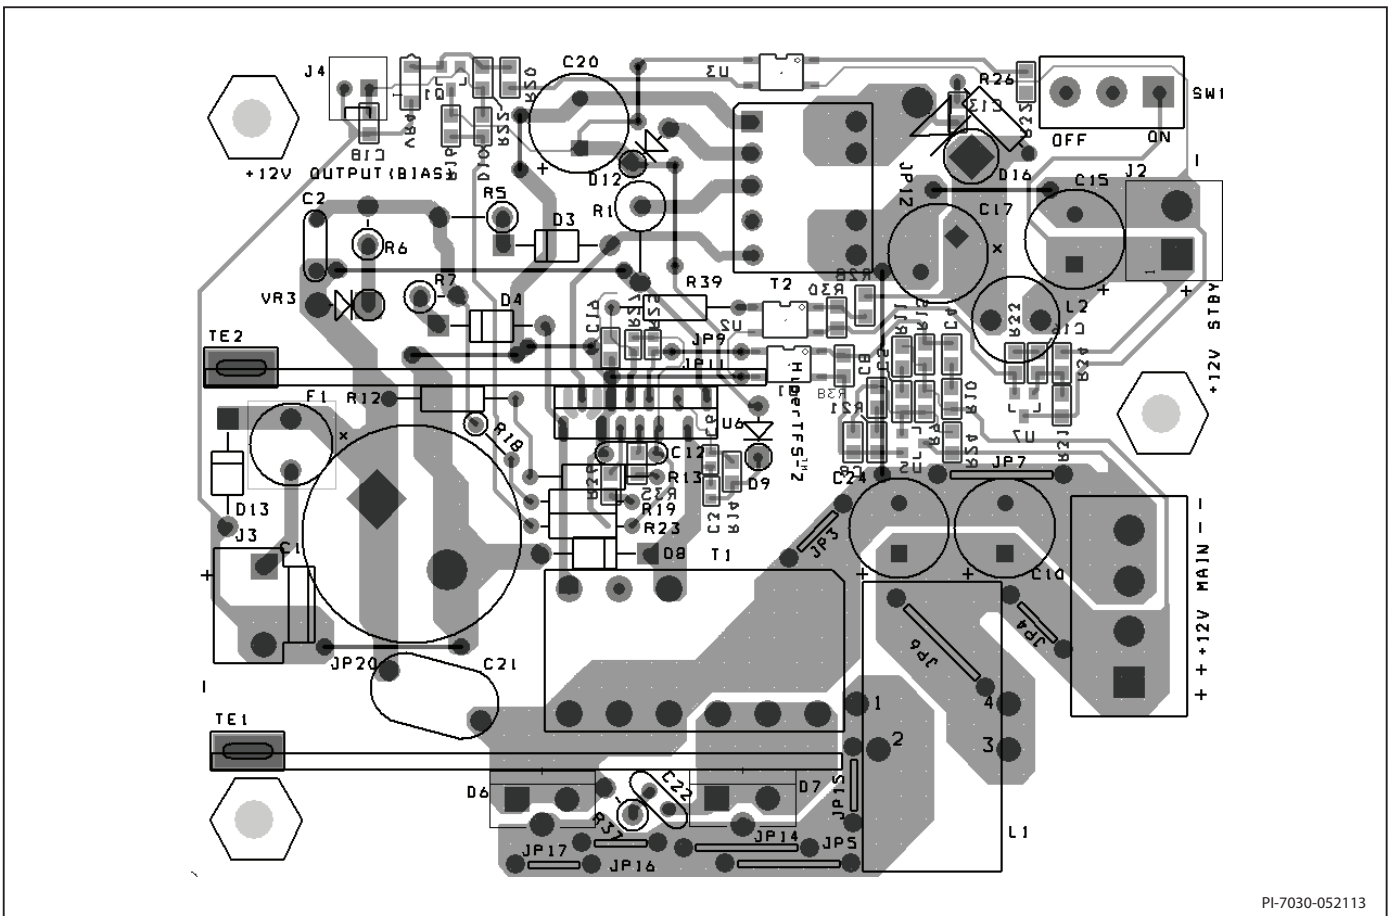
圖 30 中的設計範例 PCB 佈局電路圖。
